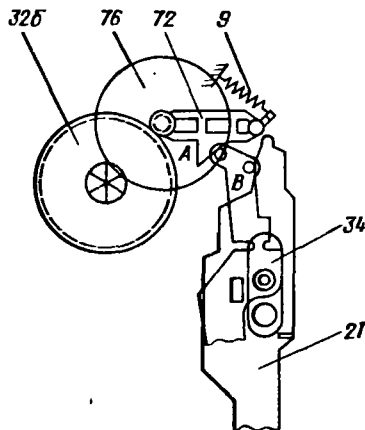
Механизм мгновенного останова магнитной ленты. (Позиционные обозначения к рис. 1.173—1.177 даны по каталогу): 2 — арретир мгновенного останова; 3 — рычажок; 4 — зубчатый сектор; 5 — пружина; 6 — шестерня автостопа; 7 — эксцентриковая шестерня; 8 — блокировочная пружина; 9 — пружина муфты сцепления; 11а — поводок; 11б — фиксирующий шуп; 12 — пластина разблокировки; 13 — штифт; 15 — пружина; 21 — рычаг мгновенного останова; 32б — приемный шпindel; 34 — пластина прижимного ролика; 72 — рычаг муфты сцепления; 76 — диск муфты сцепления; 79 — маховик с зубчатой втулкой
